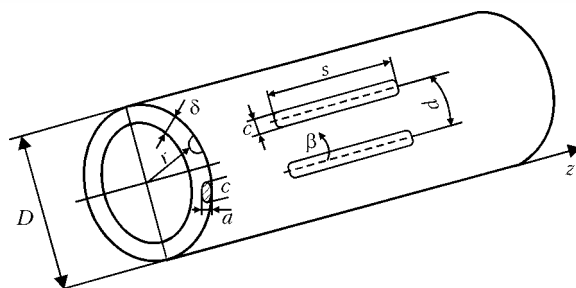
Схема цилиндрической оболочки-трубы с продольными канавочными дефектами утонения
